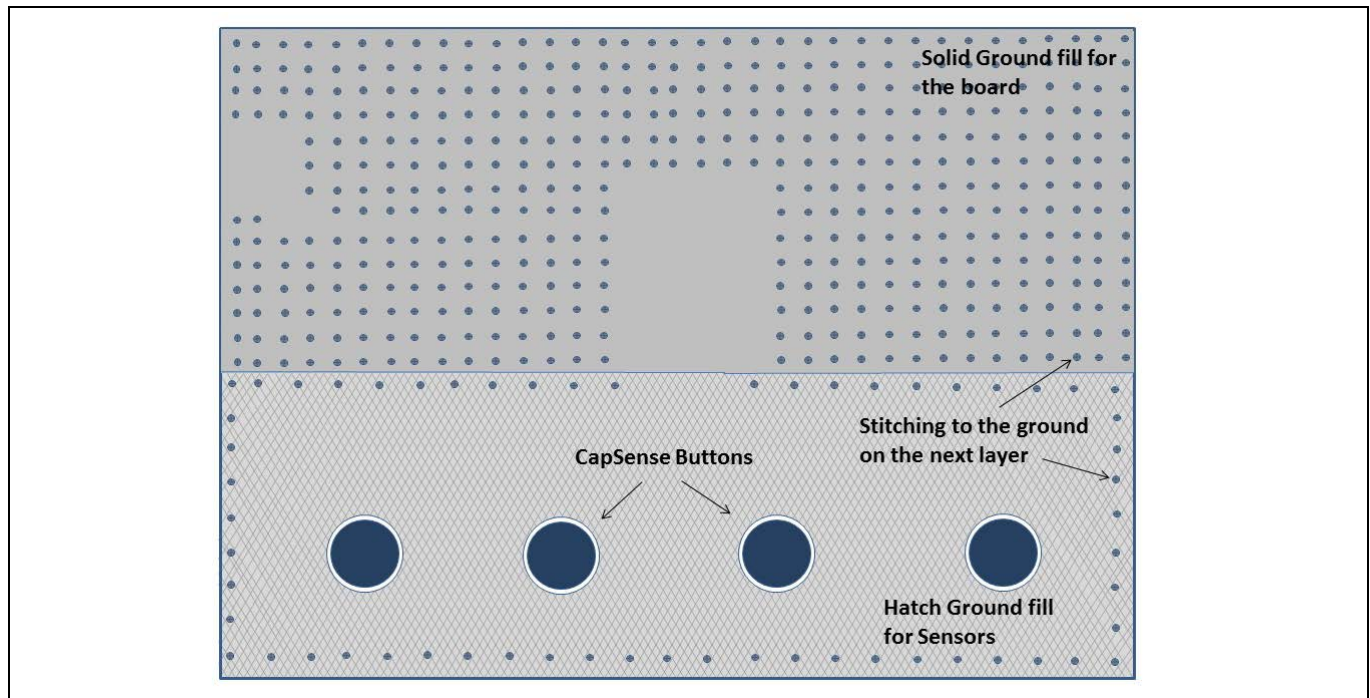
E-pad がないチップを使用する場合の PCB 最上層のレイアウト
